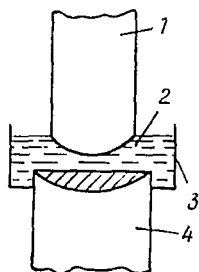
Схема приварки электрода к инвентарной головке на установке ЭСП:
